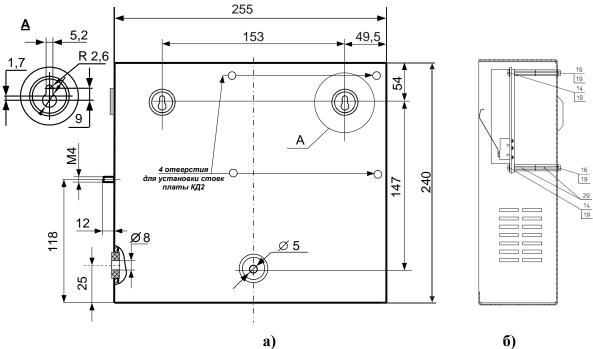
Габаритные и присоединительные размеры КД2 исп. 1. Вид сзади (а) и вид с боку (б)
